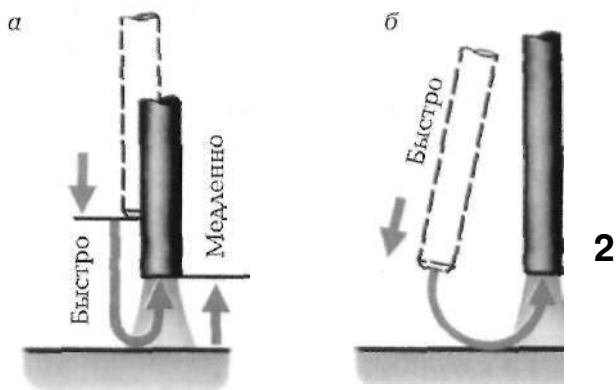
Схема зажигания сварочной дуги:
